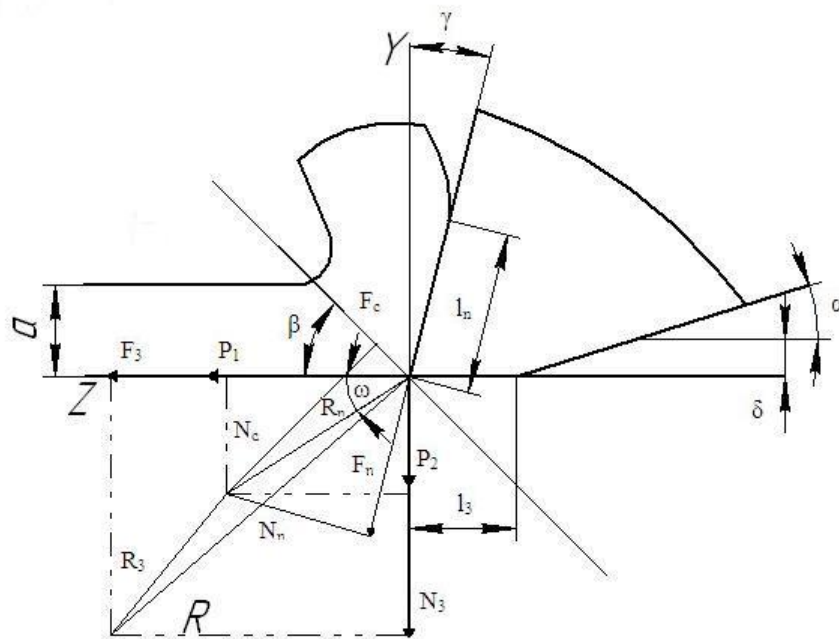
Схема сил, що діють в зоні різання [28,29]
